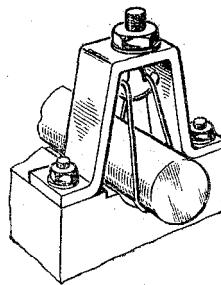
Приспособление для подъема валов при выкатке вкладышей
